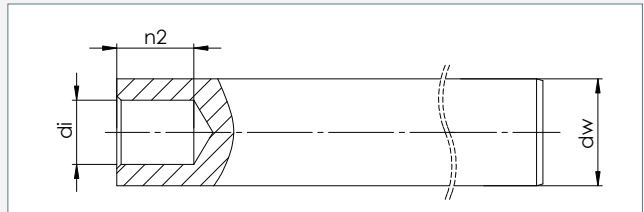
Zusammengesetzte Wellen / Compound shafts
